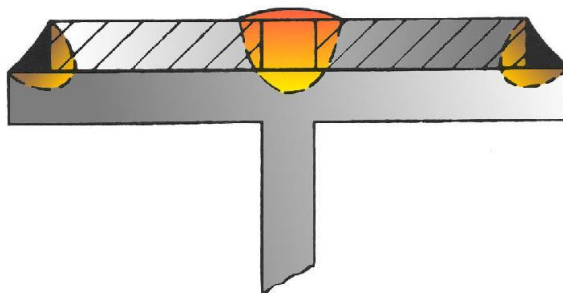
Reforço, com solda tampão, da junta previamente soldada por soldas em ângulo
